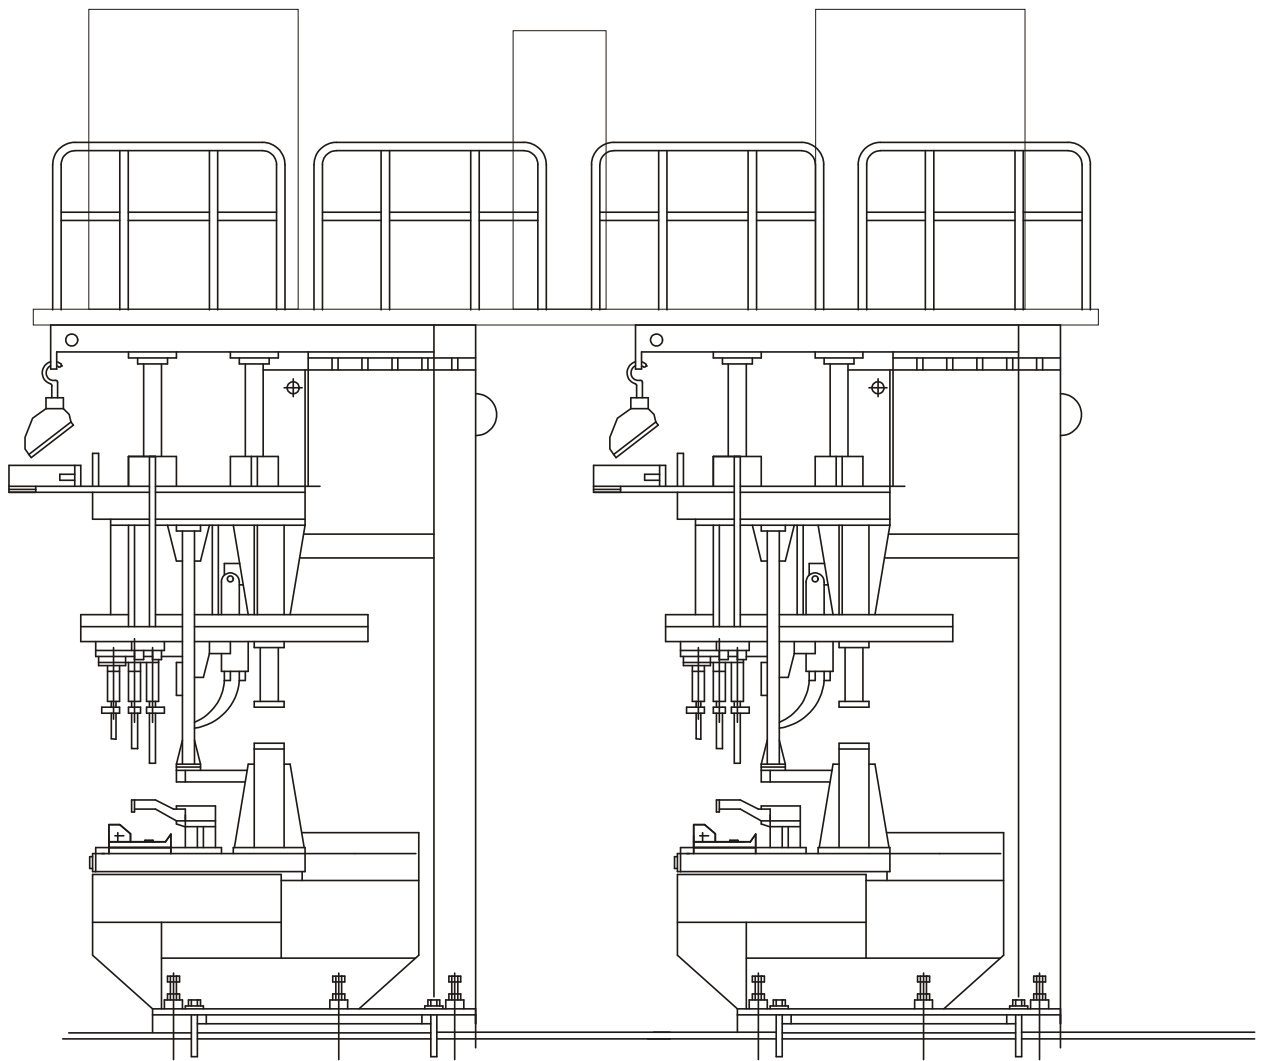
Сварка на многоэлектродных контактных сварочных машинах
